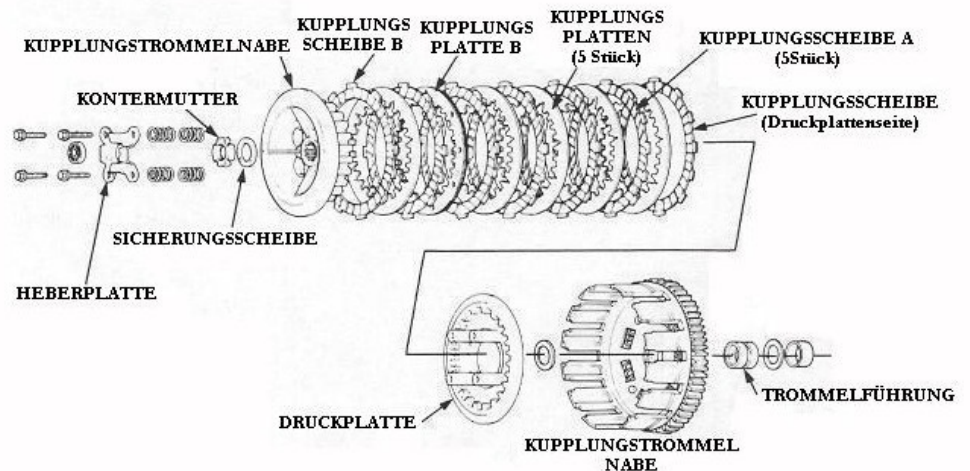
Explosionszeichnung der Kupplung mit den Originalbezeichnungen
